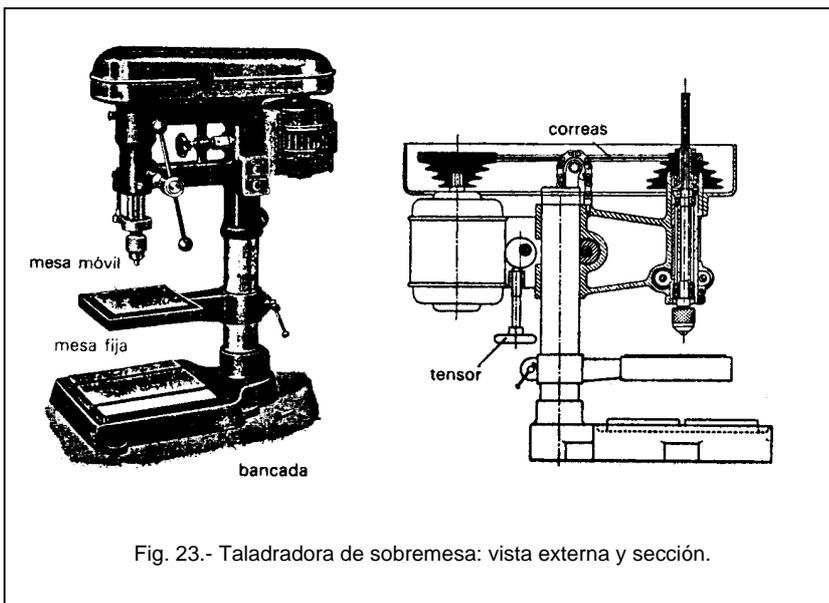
Taladradora de sobremesa: vista externa y sección.
